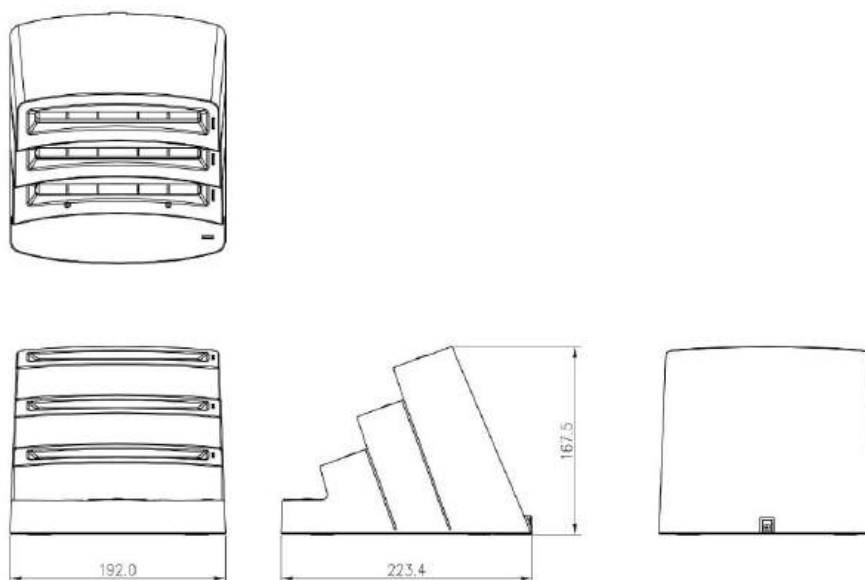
Vista ilustrativa dimensional do carregador de bateria
